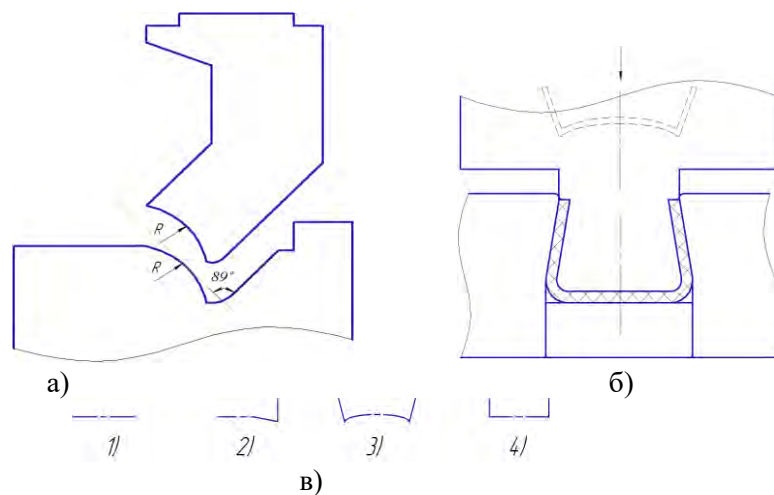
Поелементне гнуття деталі інструментом із профільованими контактними поверхнями: а – інструмент; б – калібрування; в – схеми переходів (вісь заготовки на переходах)
